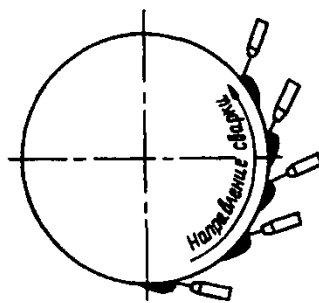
Положение горелки при сварке вертикального стыка
